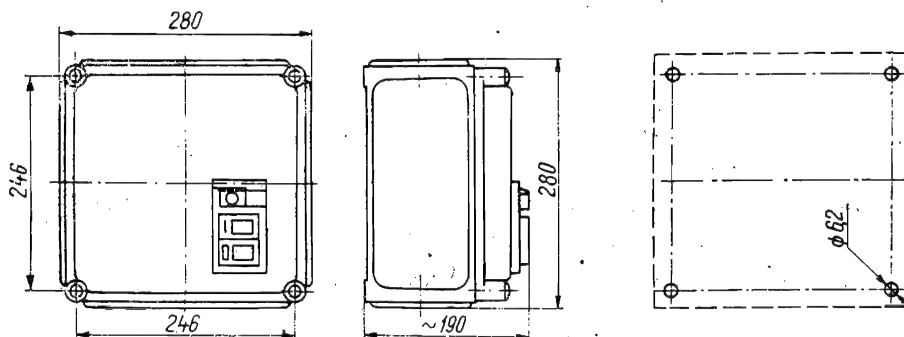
Contactor cu rele în carcasă de bachelită 63 A cod 3226 A.
